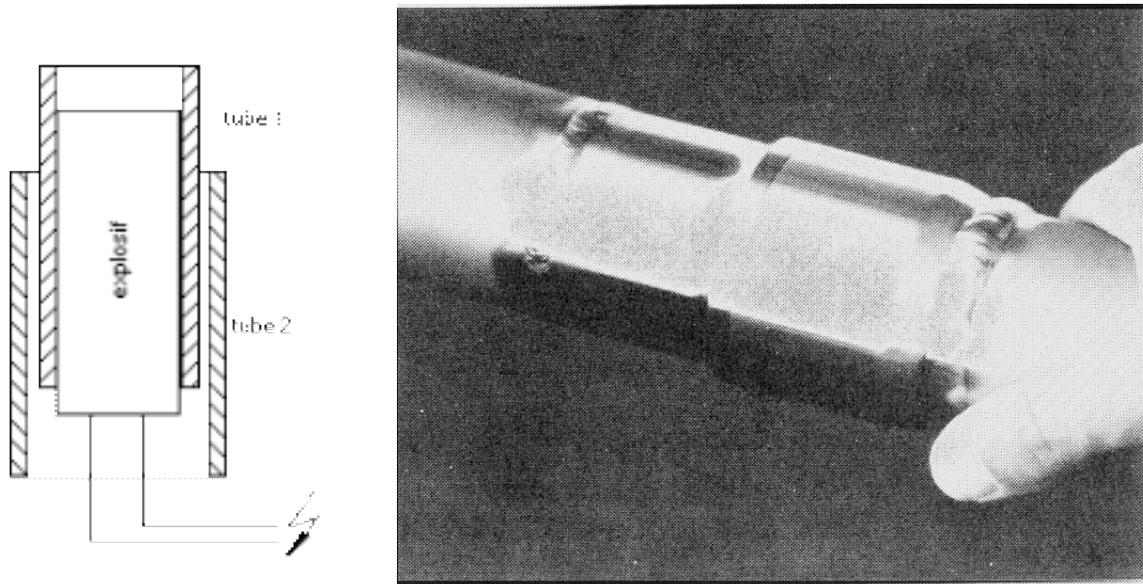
Disposition alternative pour le soudage par explosion: connexion par recouvrement de deux tubes utilisée comme adaptation entre deux tubes de matériaux dissemblables.
